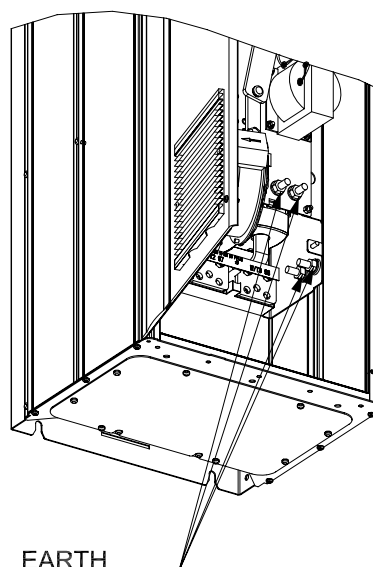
Compact IP 00 (Chassis) met werkschakelaar, zekering en RFI-filter, framegrootte D4
